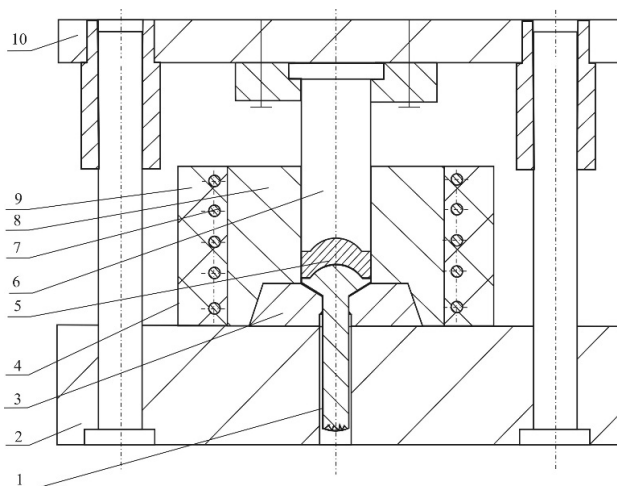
Штамп для выдавливания прутка из прессовок: 1 – выдавливаемый пруток; 2 – плита нижняя; 3 – вставка; 4 – печь; 5 – прессовка; 6 – пуансон; 7 – нагреватели; 8 – матрица; 9 – теплоизоляция; 10 – верхняя плита
